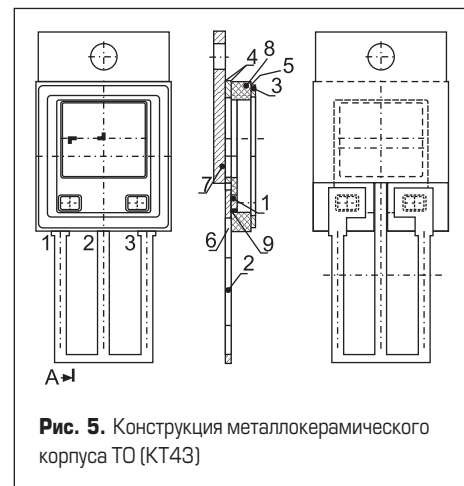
Конструкция металлокерамического корпуса ТО (КТ43)
